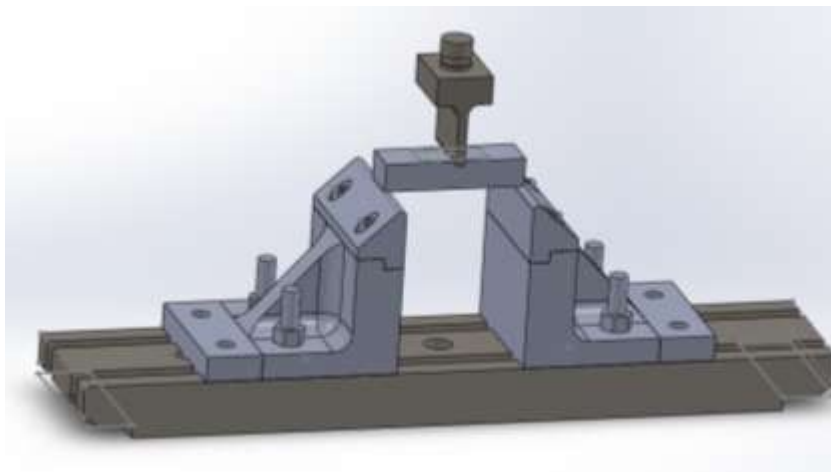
7 Vista isométrica de ensamblaje de plataforma
